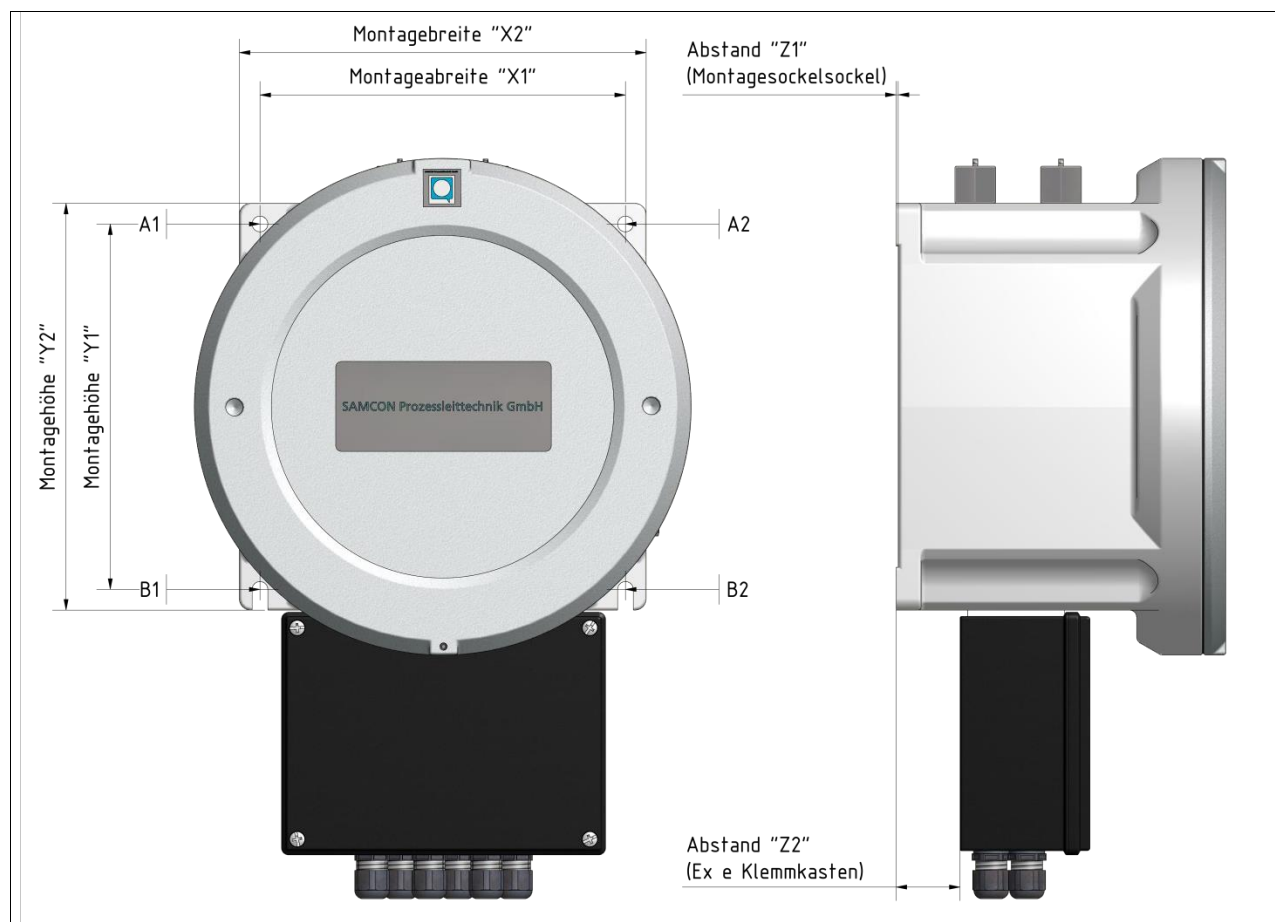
Монтажные и установочные размеры ExConnection Rail
